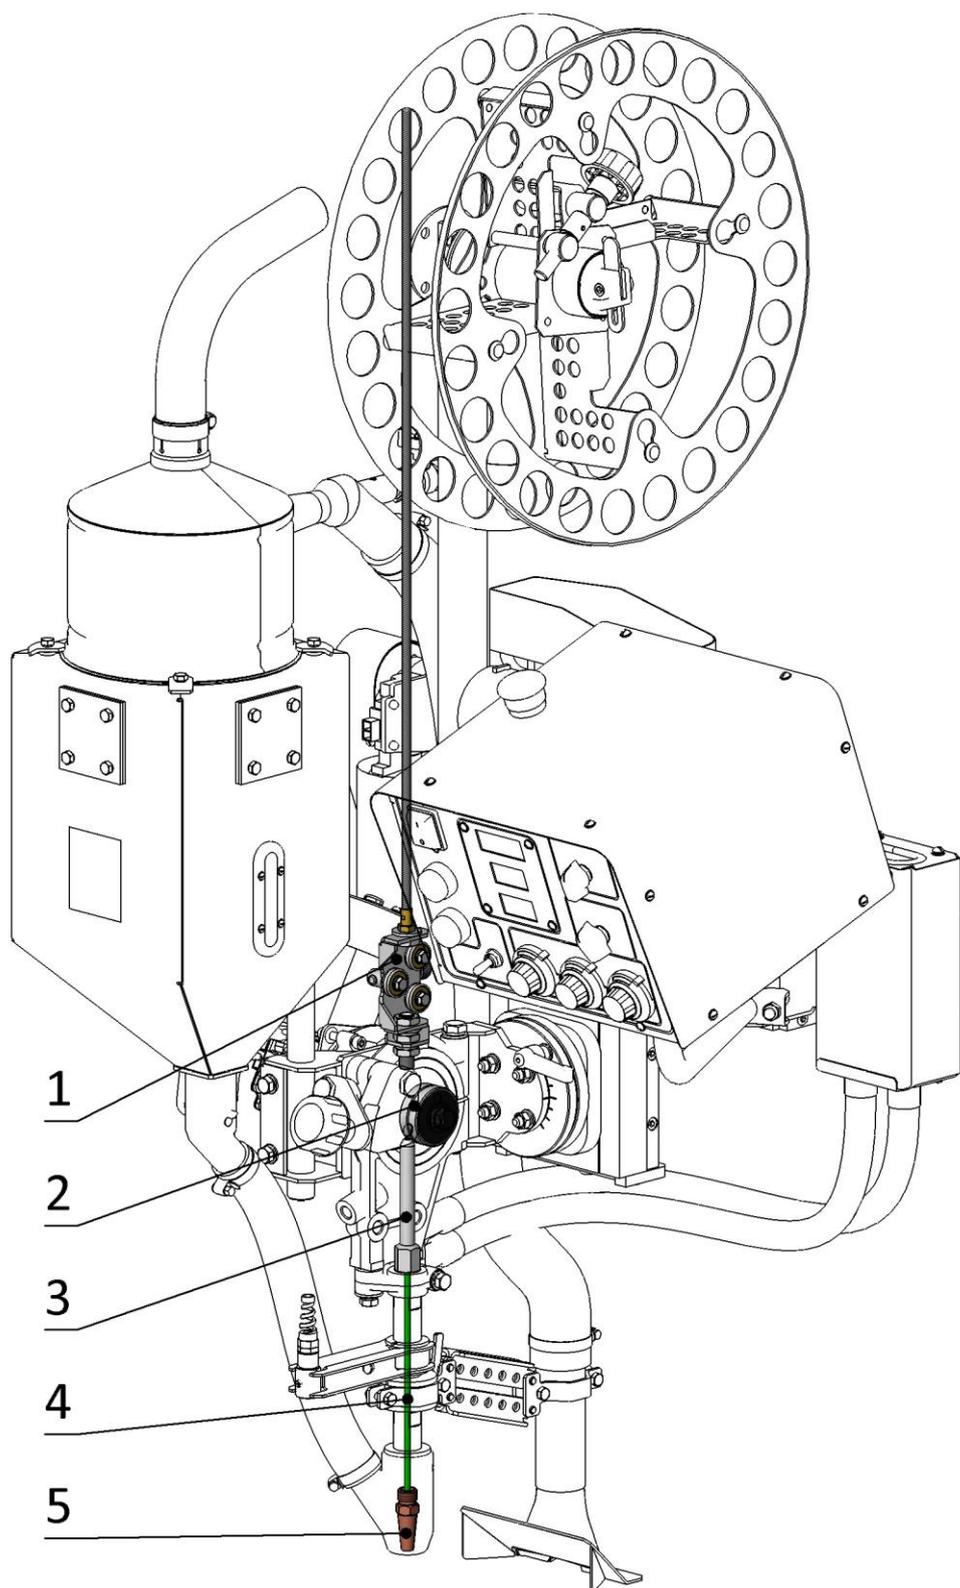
Комплект для сварки проволокой Ø2 мм.
